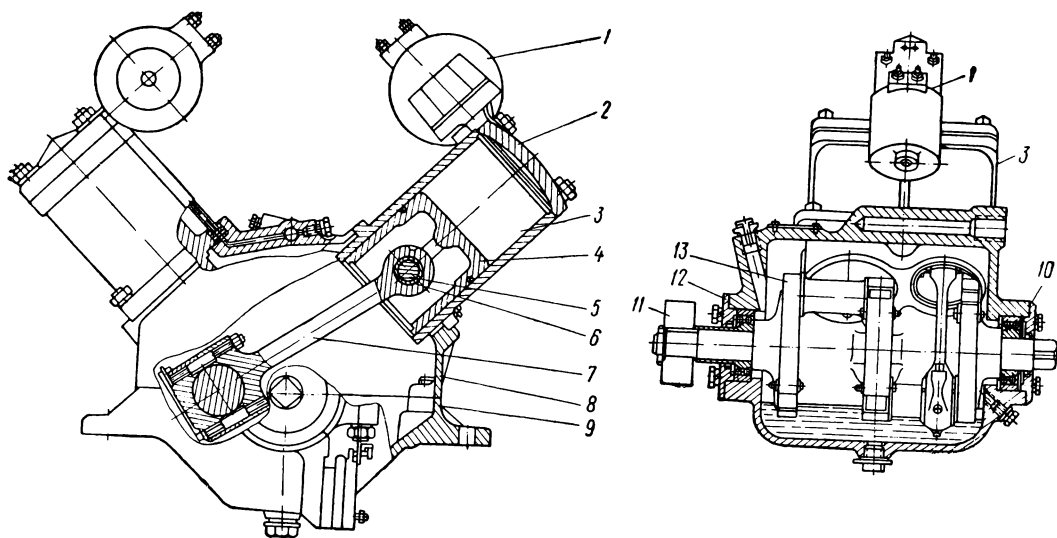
Пневматический двигатель главного контроллера и переключателя ступеней ослабления поля электровозов ЧС2:
